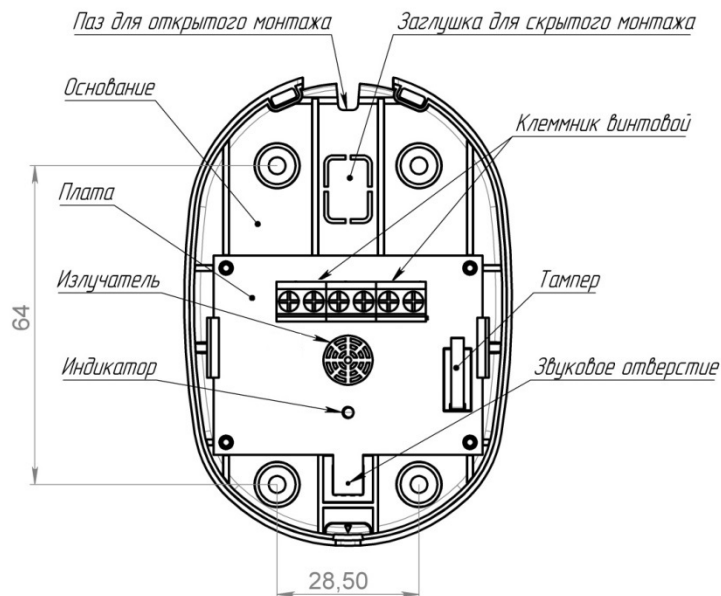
Конструкция и установочные размеры извещателя.
